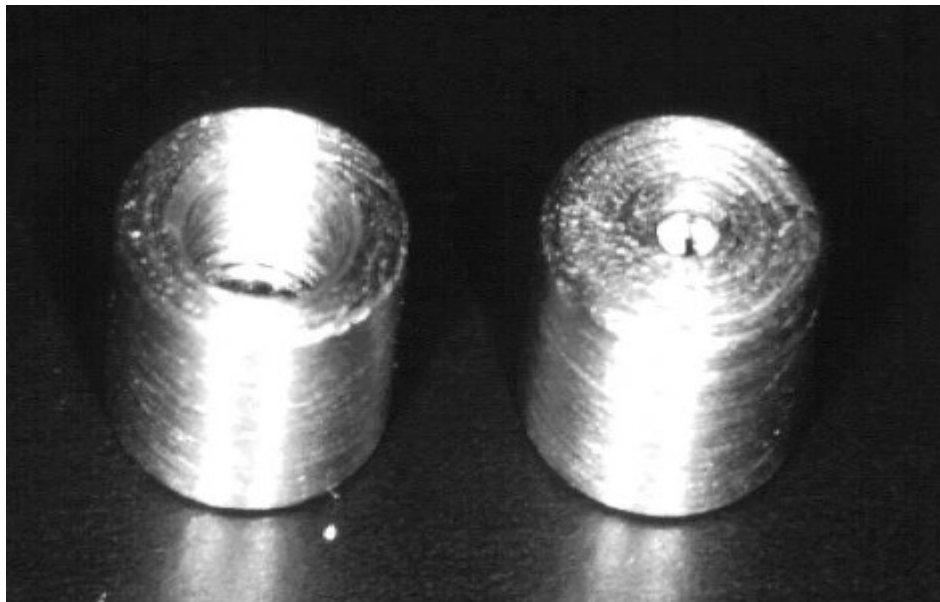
Fotos der Einschraubhülsen. Auf der linken Seite ist die Hülse von oben gezeigt, in der Tiefe ist das Innengewinde erkennbar, in das der Aufnahme für das Stahlseil gedreht wurde. Rechts ist die Unterseite mit dem Loch erkennbar, durch das der Schraubenschaft geführt wurde.
